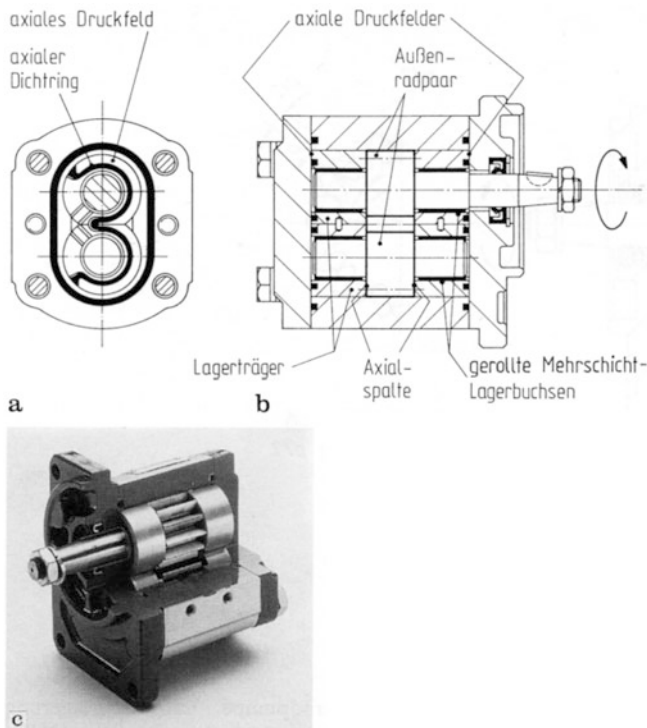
Außenzahnradpumpe mit hydraulischem Spaltausgleich, saugseitige radiale Abdichtung (S, Buchsenpumpe, Bosch Rexroth). a Gehäusedeckel, axiale Druckkompensation mittels Dichtelementen (Lagerträgern); b Längsschnitt, radiale (passive) Druckkompensation durch Zahnkopfanlage an saugseitiger Laufbahn im Pumpengehäuse; c Schnittmodell
